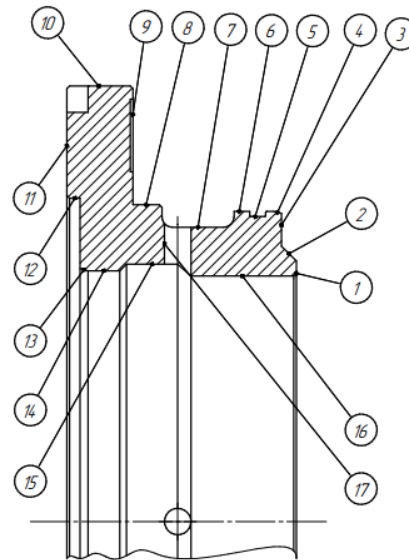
Поверхні базування деталі «Втулка фланцева» у вузлі
